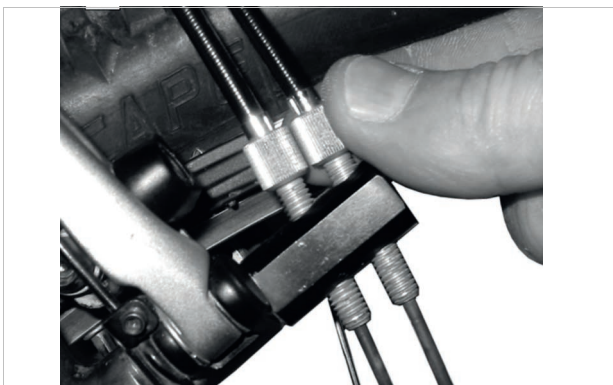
ROHLOFF-Naben Versionen mit interner Schaltansteuerung haben die Zugeinsteller am Zuggegenhalter
